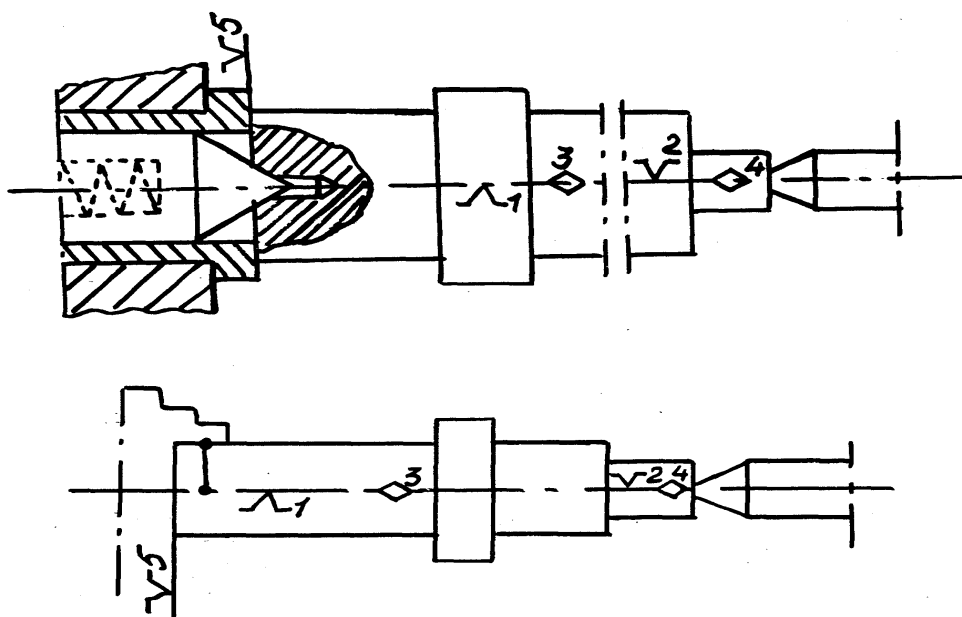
Реалізація схем базування заготовок типу обертання з використанням віссю, як бази
